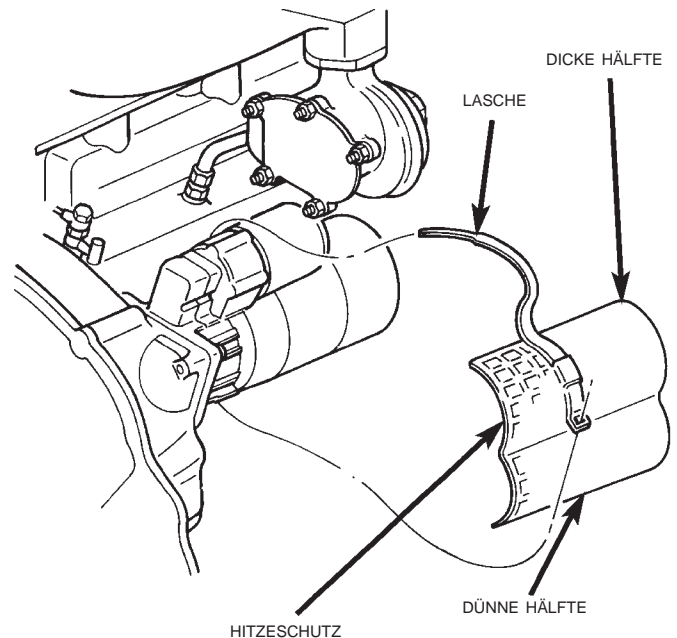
Befestigung des Anlassers - 2.5L-Dieselmotor
